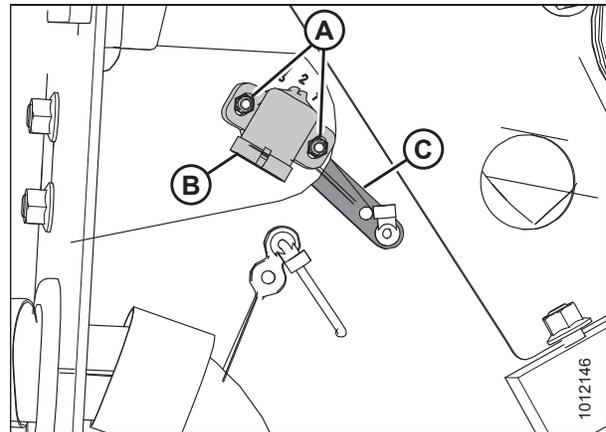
Conjunto do sensor de altura da plataforma - lado esquerdo
